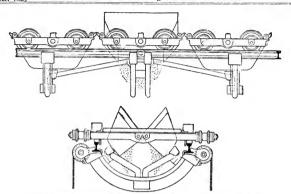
Becherkette mit Entleerungsvorrichtung, Bauart der Steel Cable Engineering Co.
